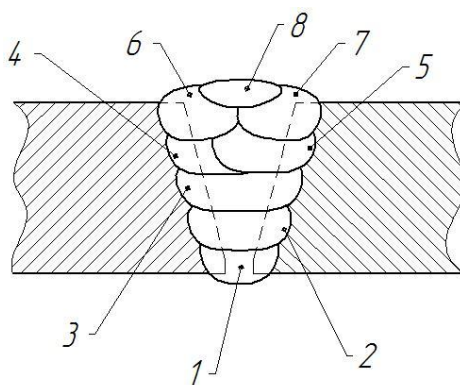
Сварное соединение и порядок наложения валиков в
